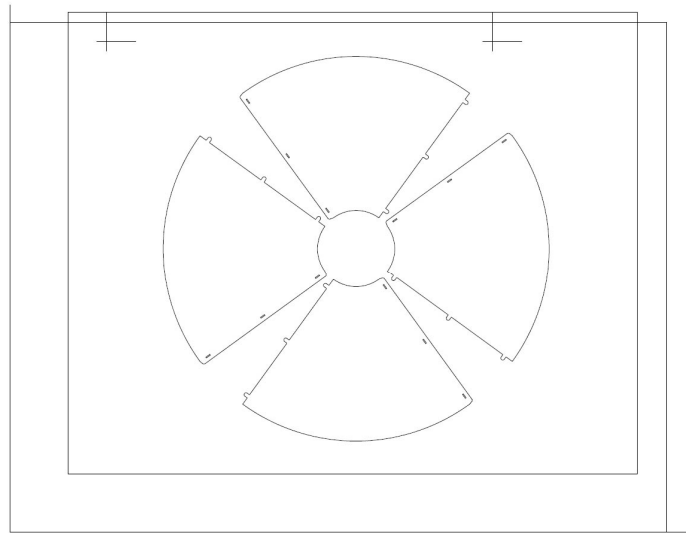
Plano de distribución de figuras cónicas femeninas
